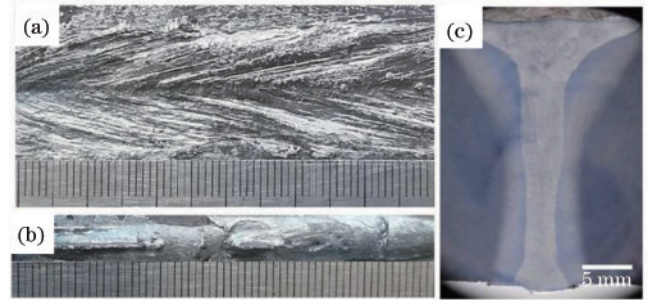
焊缝及横截面宏观形貌。(a)正面形貌;(b)背面形貌;(c)接头横截面
